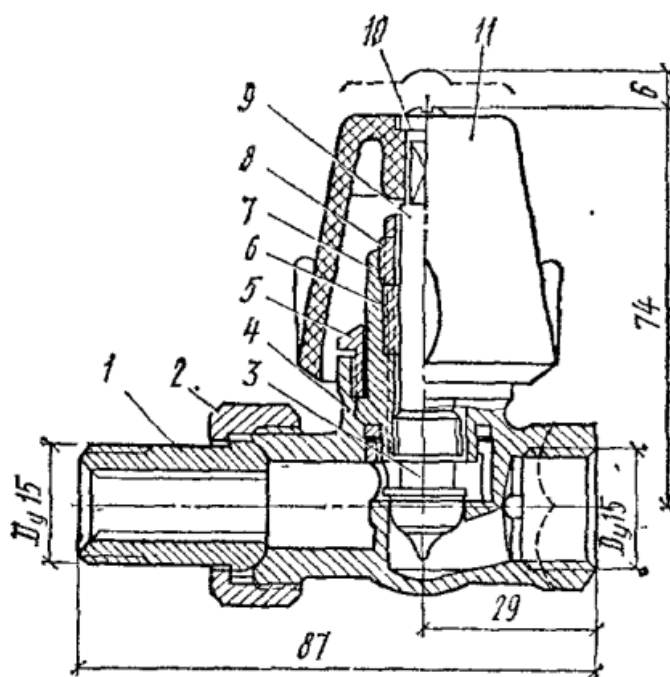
Кран двойной регулировки вентильного типа: 1 – патрубок с наружной резьбой; 2 – соединительная гайка; 3 – клапан; 4 – корпус; 5 – гайка крышки; 6 – набивка; 7 – крышка; 8 – гайка уплотнителя шпинделя; 9 – шпиндель; 10 – винт; 11 – маховик
